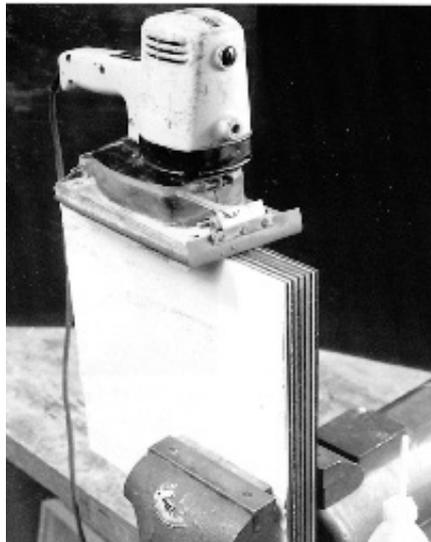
Schleifen der Kante eines Zuschnittpakets mit Schwingschleifer
